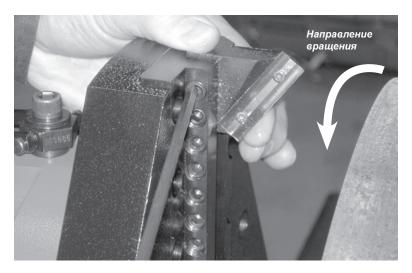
Вставьте резец в резцедержатель и затяните установочные винты. Убедитесь в установке режущей кромки по направлению вращения, см. изображение.
